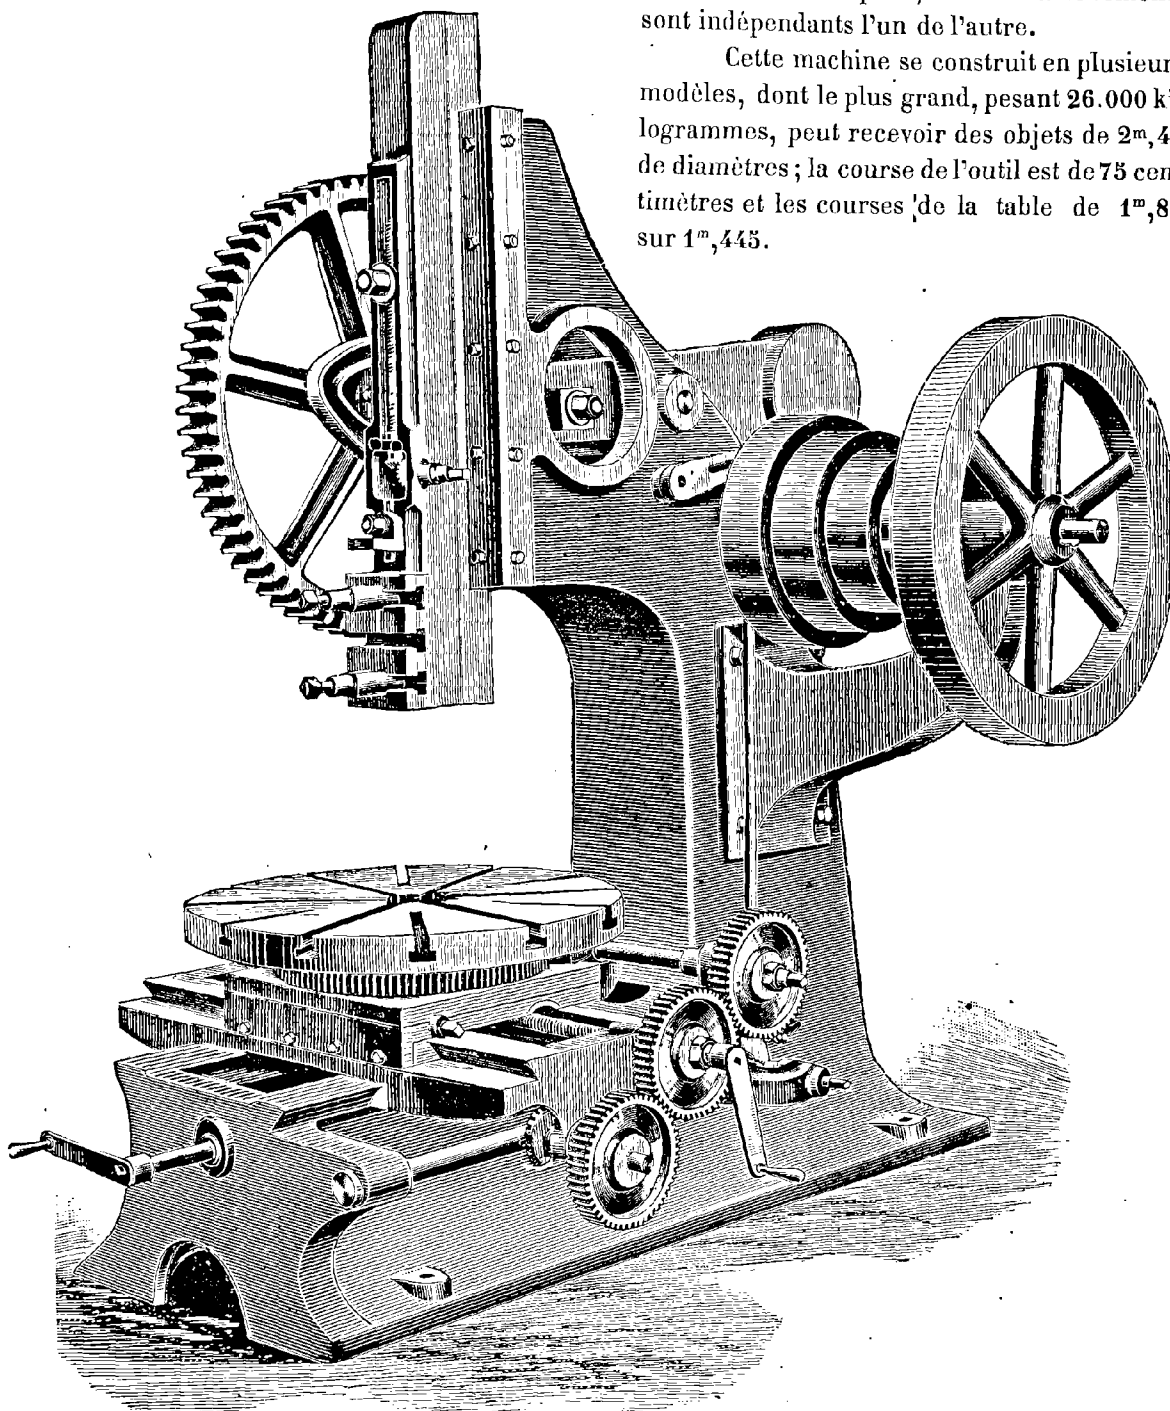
Machine à mortaiser à mouvement latéral de M. Lucas.
